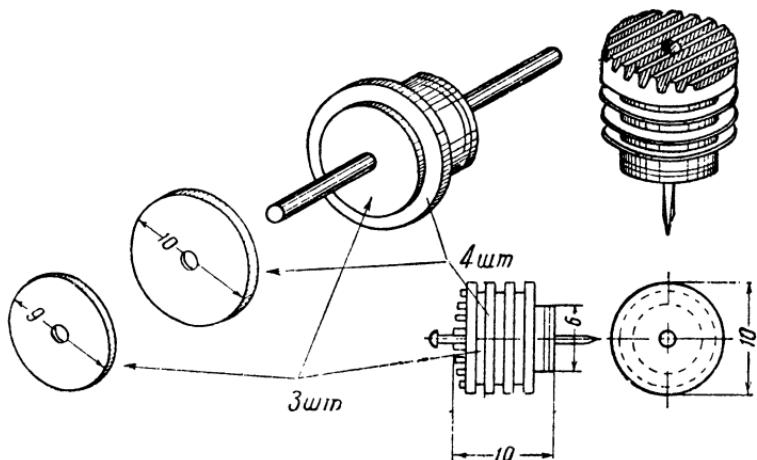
Шаблоны винта (вид сбоку и спереди). Процесс изготовления винта.
